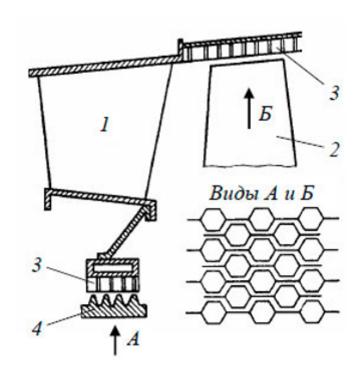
Сотовые уплотнения газовых турбин: *1* – направляющий аппарат; *2* – рабочая лопатка; *3* – сотовые уплотнения; *4* – уплотнительные гребни ротора
